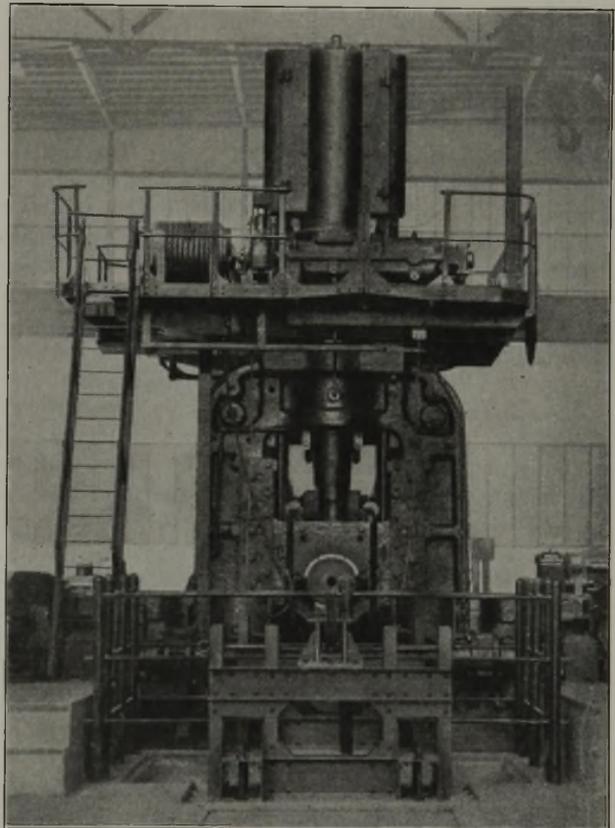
1000er Block- und Brammenstraße, ausgerüstet mit Kunstharz-Preßstofflagern.
